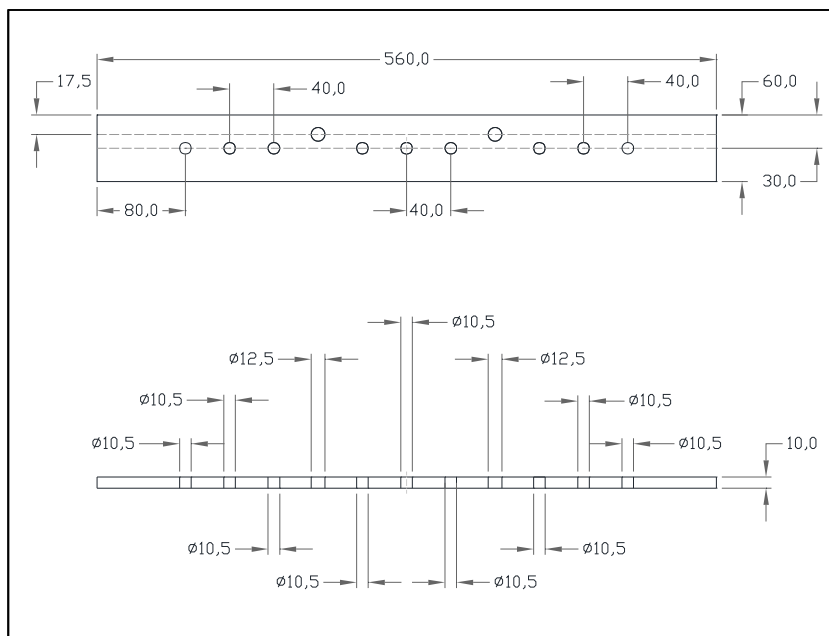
Barra de terra (plana) para caixa de inspeção pré-fabricada do tipo E
